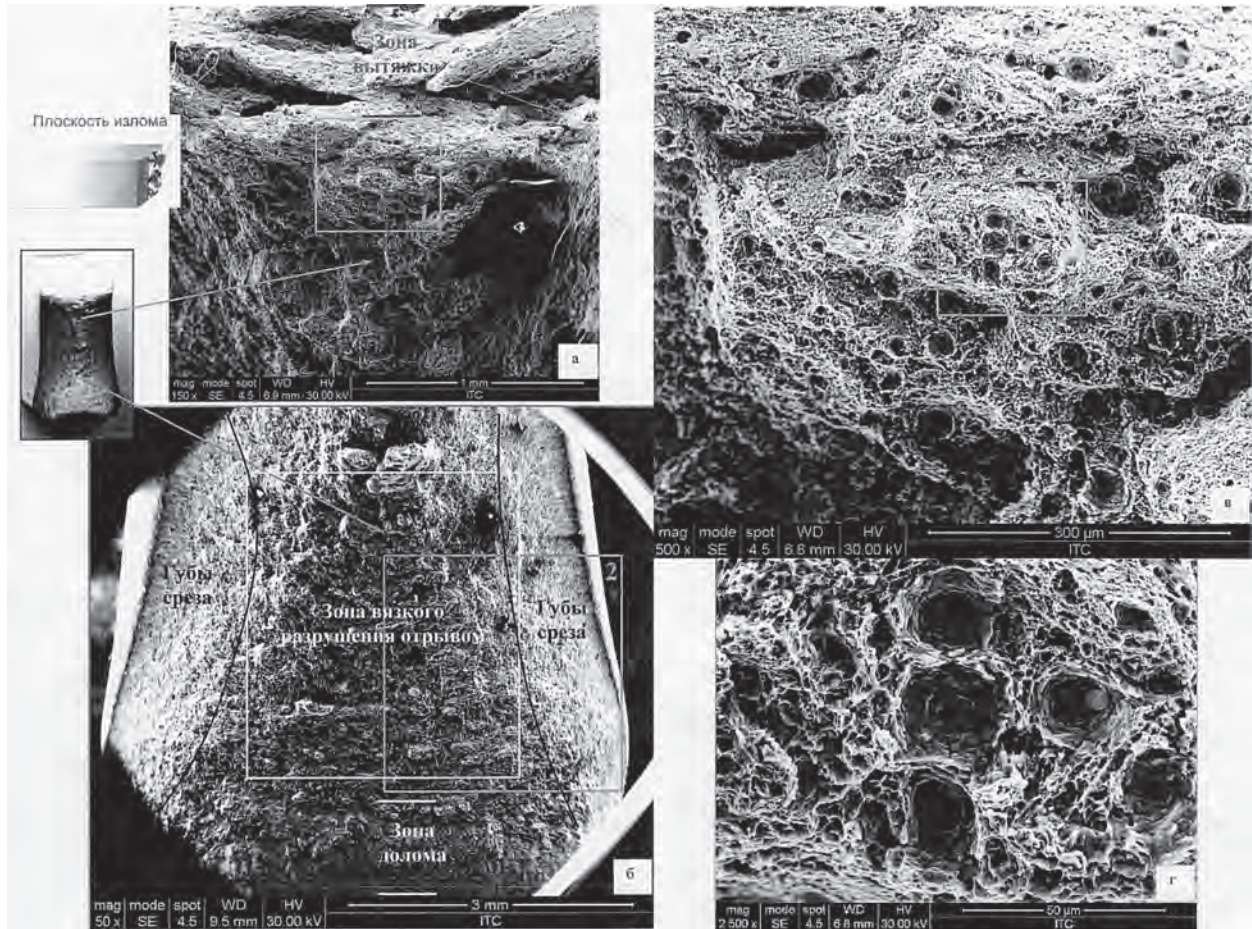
Вид излома образца металла бесшовной нефтегазопроводной трубы из стали марки 20А плавки № 335591 после испытаний на ударную вязкость: а – x150; б – x50; в – x500; г – x2500
